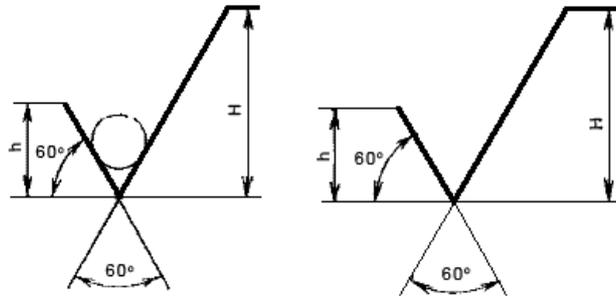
Знаки условного обозначения шероховатости поверхности
